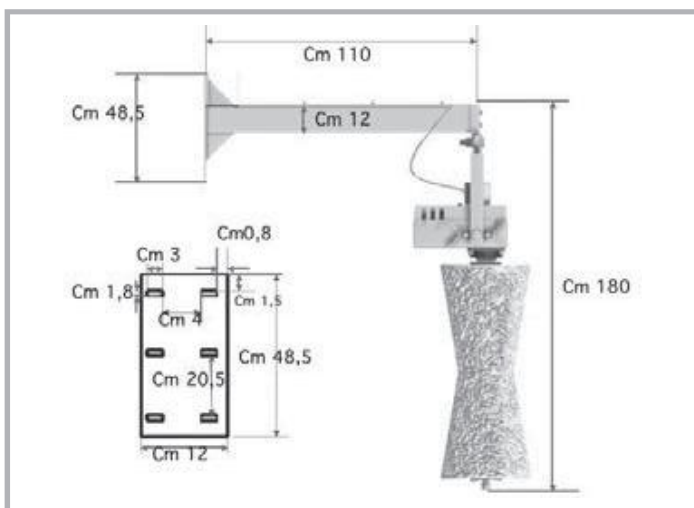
CowCleaner Swing : Montiert mit Installationsmaßen
